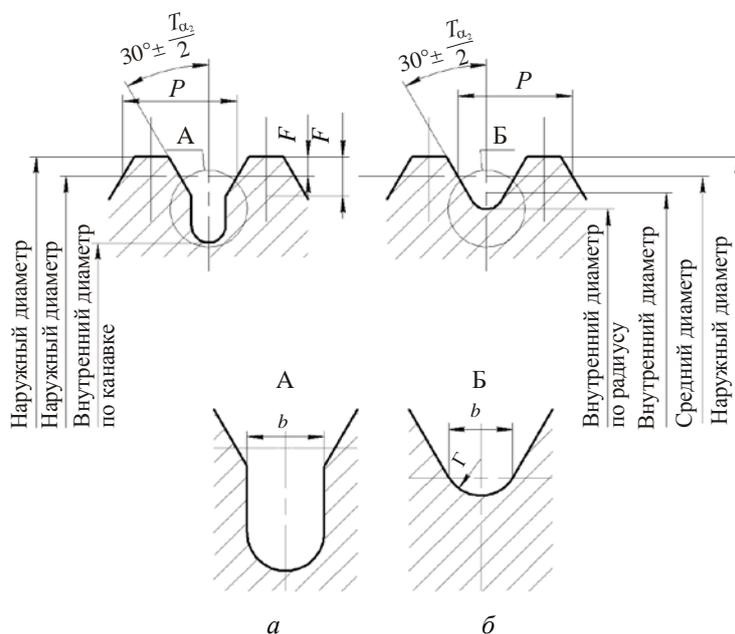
Укороченный профиль резьбы калибров-пробок для метрической резьбы:
